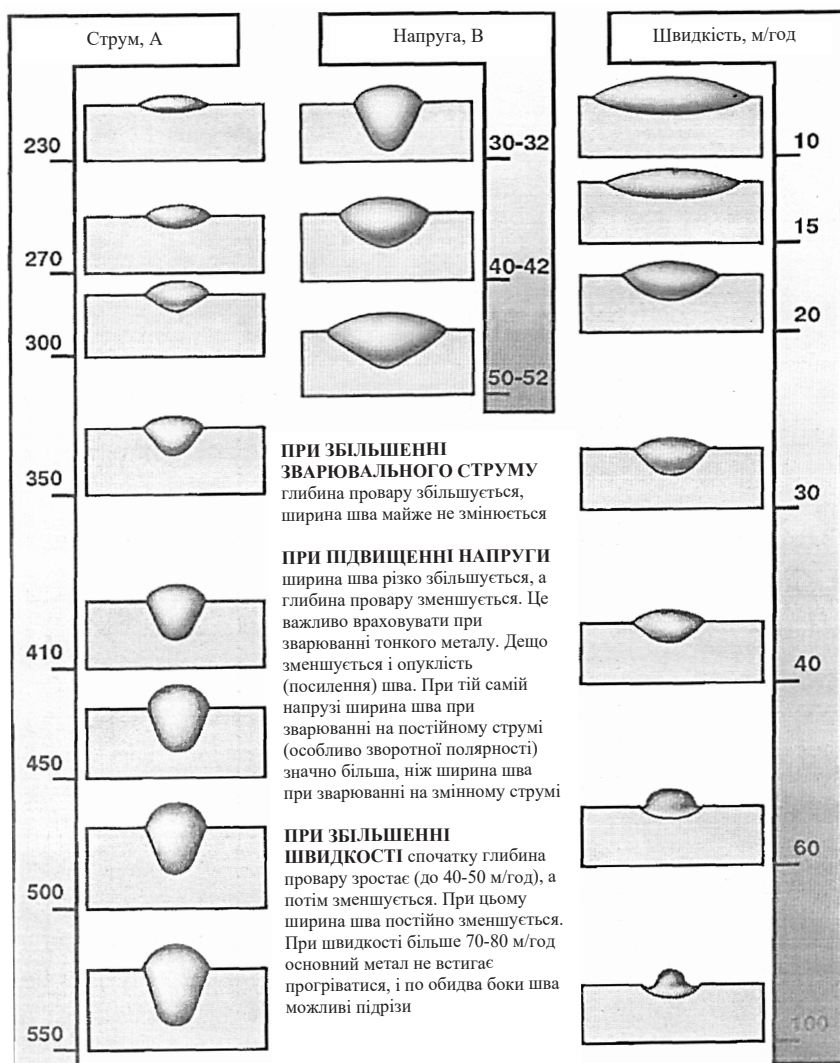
Вплив струму, напруги та швидкості зварювання на форму та розміри зварного шва
